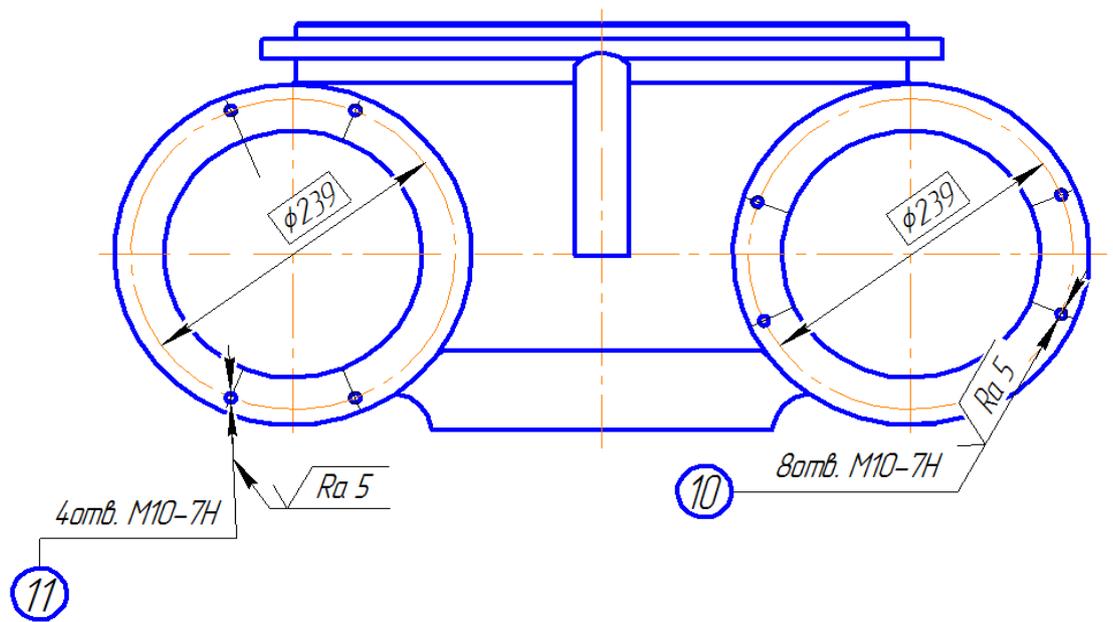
Эскиз детали «Корпус водомасляного охладителя»
